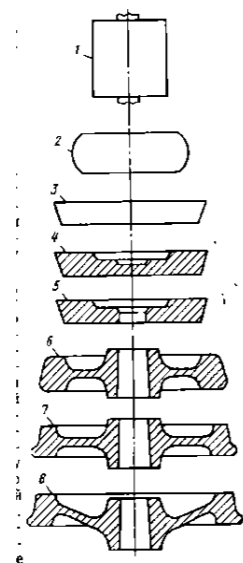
Схема деформации заготовок на прессопрокатных линиях Нижнеднепровского трубопрокатного завода и Выксунского металлургического комбината: 1 – заготовка; 2 – свободная осадка; 3 – осадка в кольце; 4 – разгонка; 5 – штамповка; 6 – прокатка; 7 – выгибка диска и калибровка; 8 – прошивка отверстия
